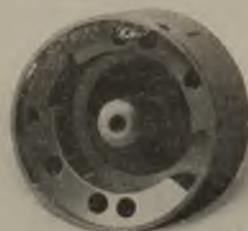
Steuermechanismus der Bohrmaschinen der Pratt Machinery Co., St. Louis.
